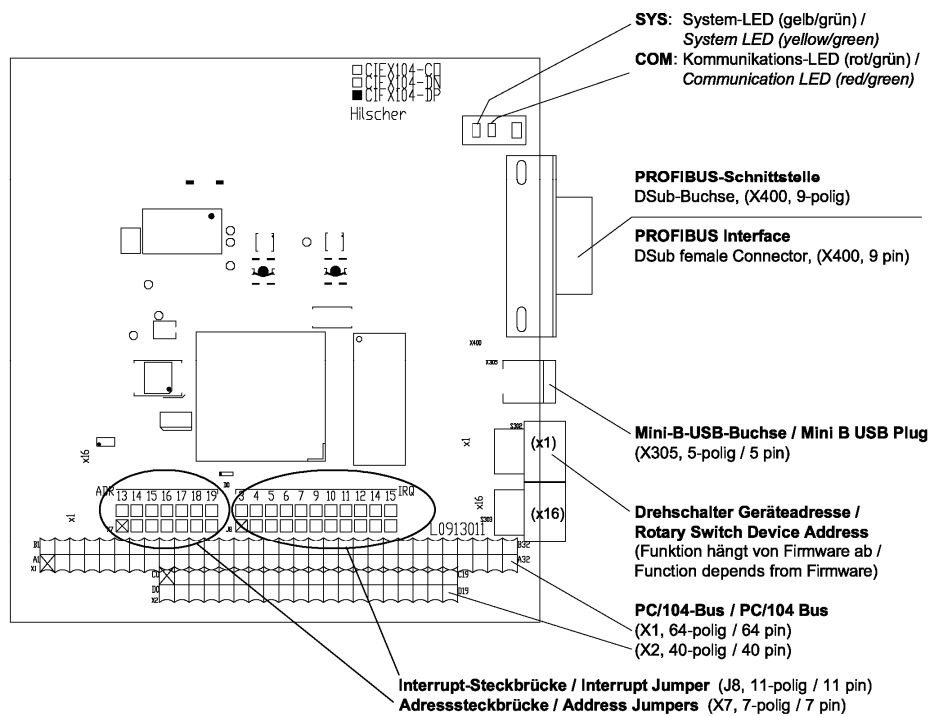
Gerätezeichnung CIFX 104-DP-R
